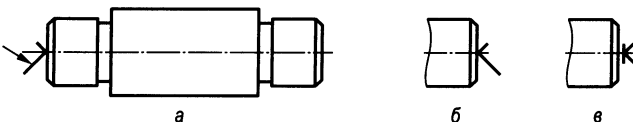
Обозначение центровых отверстий на рабочем чертеже:
